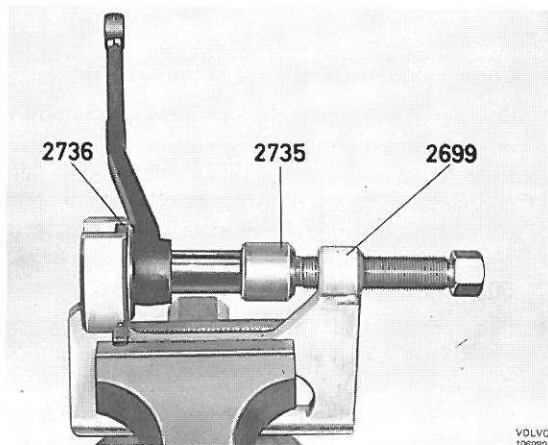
Montage de la bague caoutchouc, bras intermédiaire
